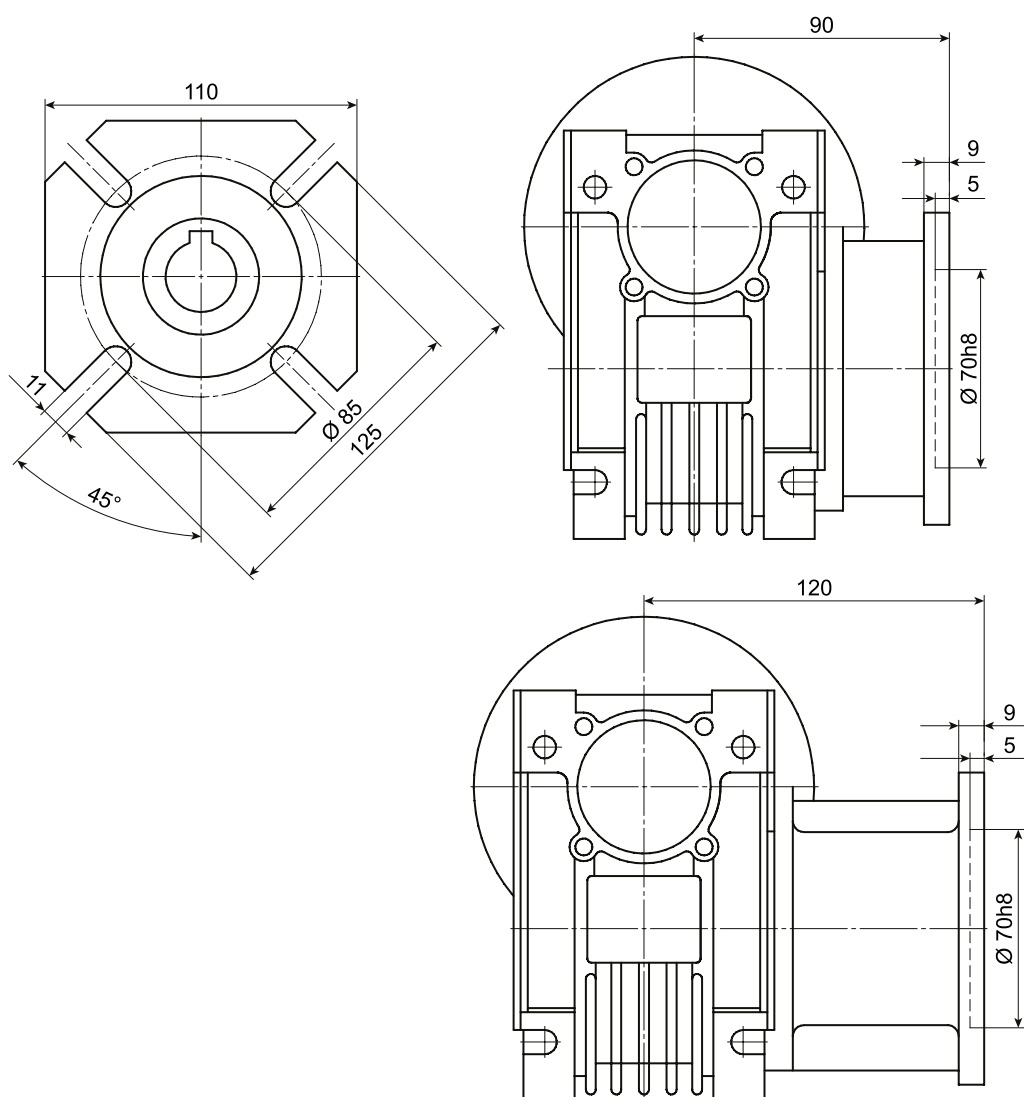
Габаритные размеры боковых фланцев FA и FB
